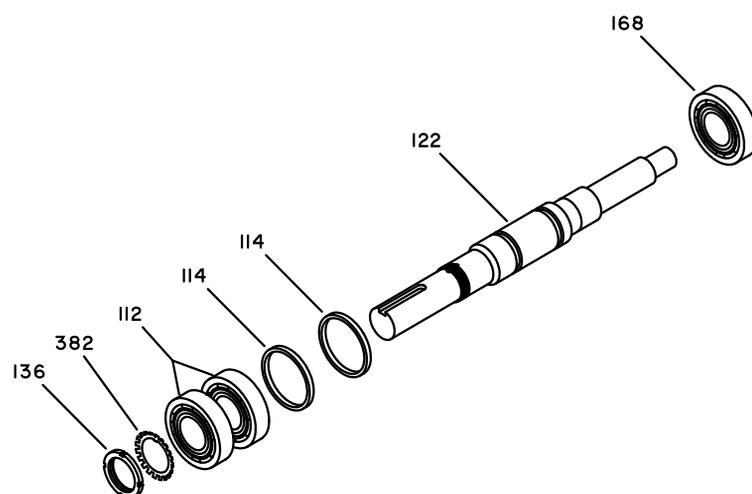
Регулировочные шайбы торцевой крышки упорного подшипника
